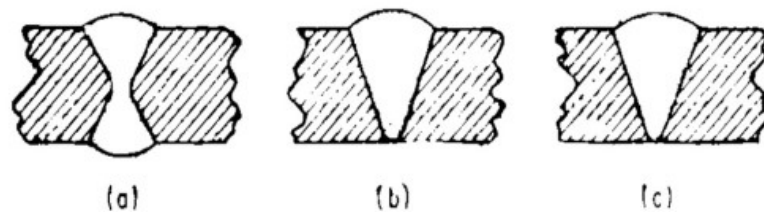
Tipos de soldadura. (a) Junta por ensamble. Soldadura doble. (b) Junta por ensamble. Soldadura simple con banda de respaldo que se puede retirar. (c) Junta por ensamble. Soldadura simple sin resguardo.
